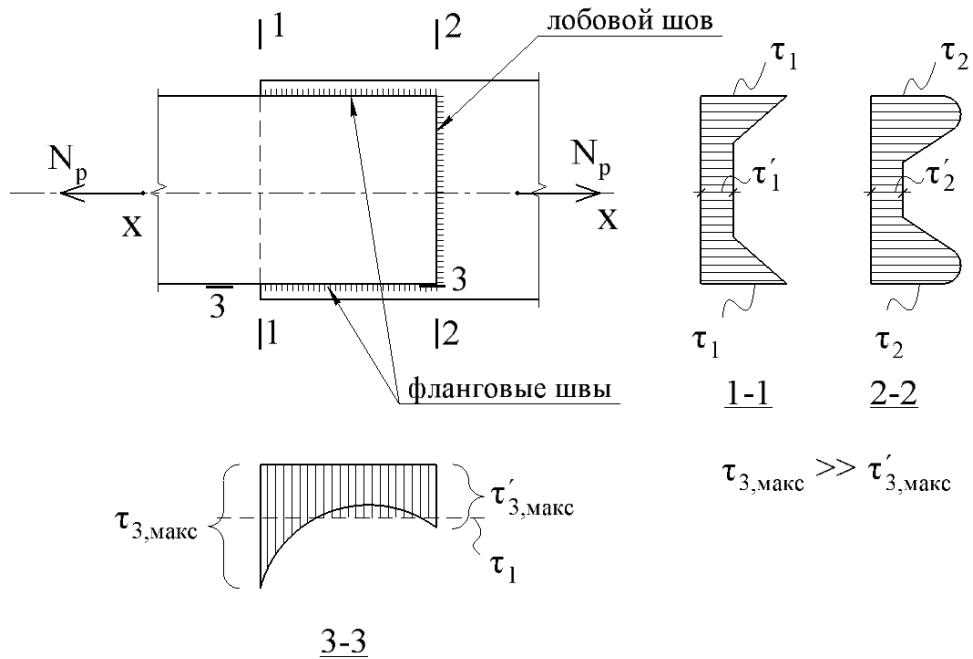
Схема сварного соединения на угловых швах, нагруженного центральной силой растяжения
